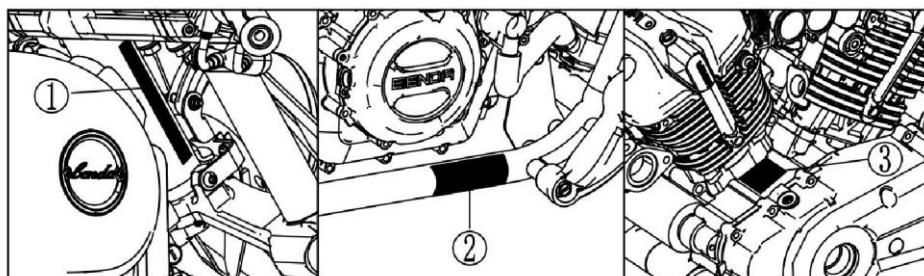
Расположение заводской таблички, номера VIN и номера двигателя
